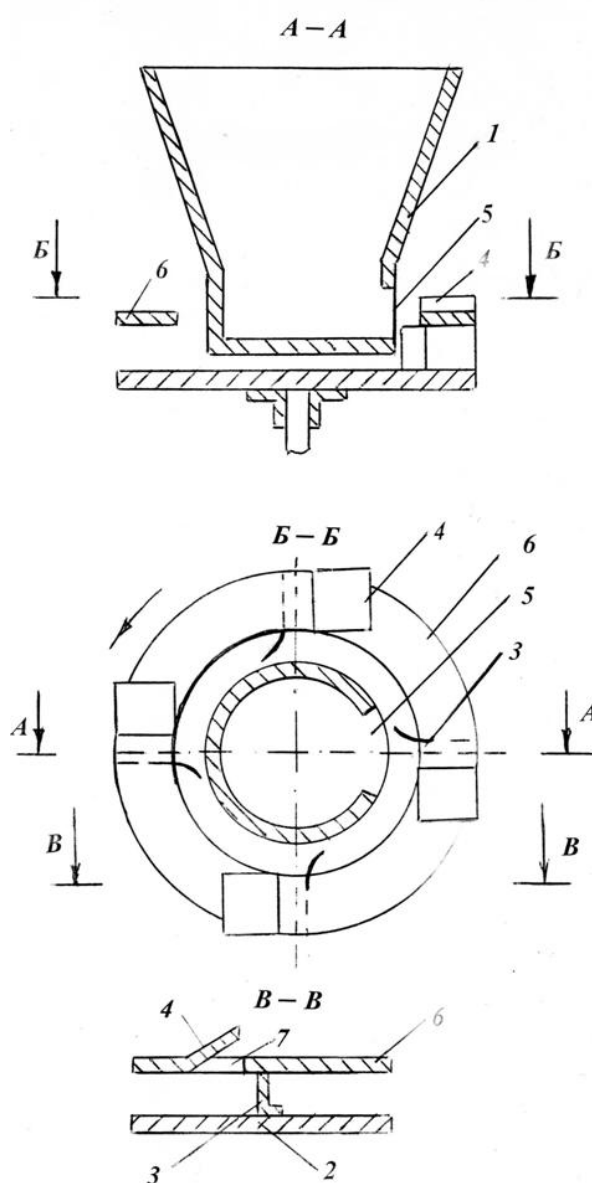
Однодисковый центробежный аппарат с подачей материала вдоль лопаток: 1- бункер; 2- рассеивающий диск; 3-внутренний торцевой
